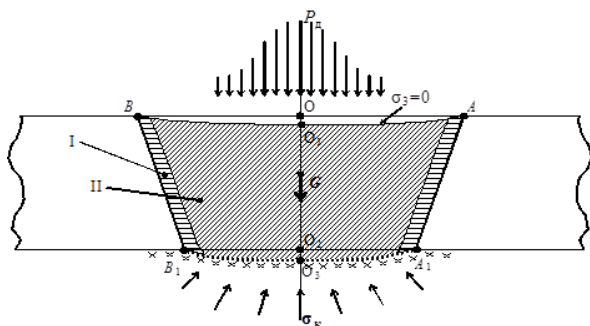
Силы, действующие на сварочную ванну при дуговой сварке (сечение, перпендикулярное направлению сварки):
